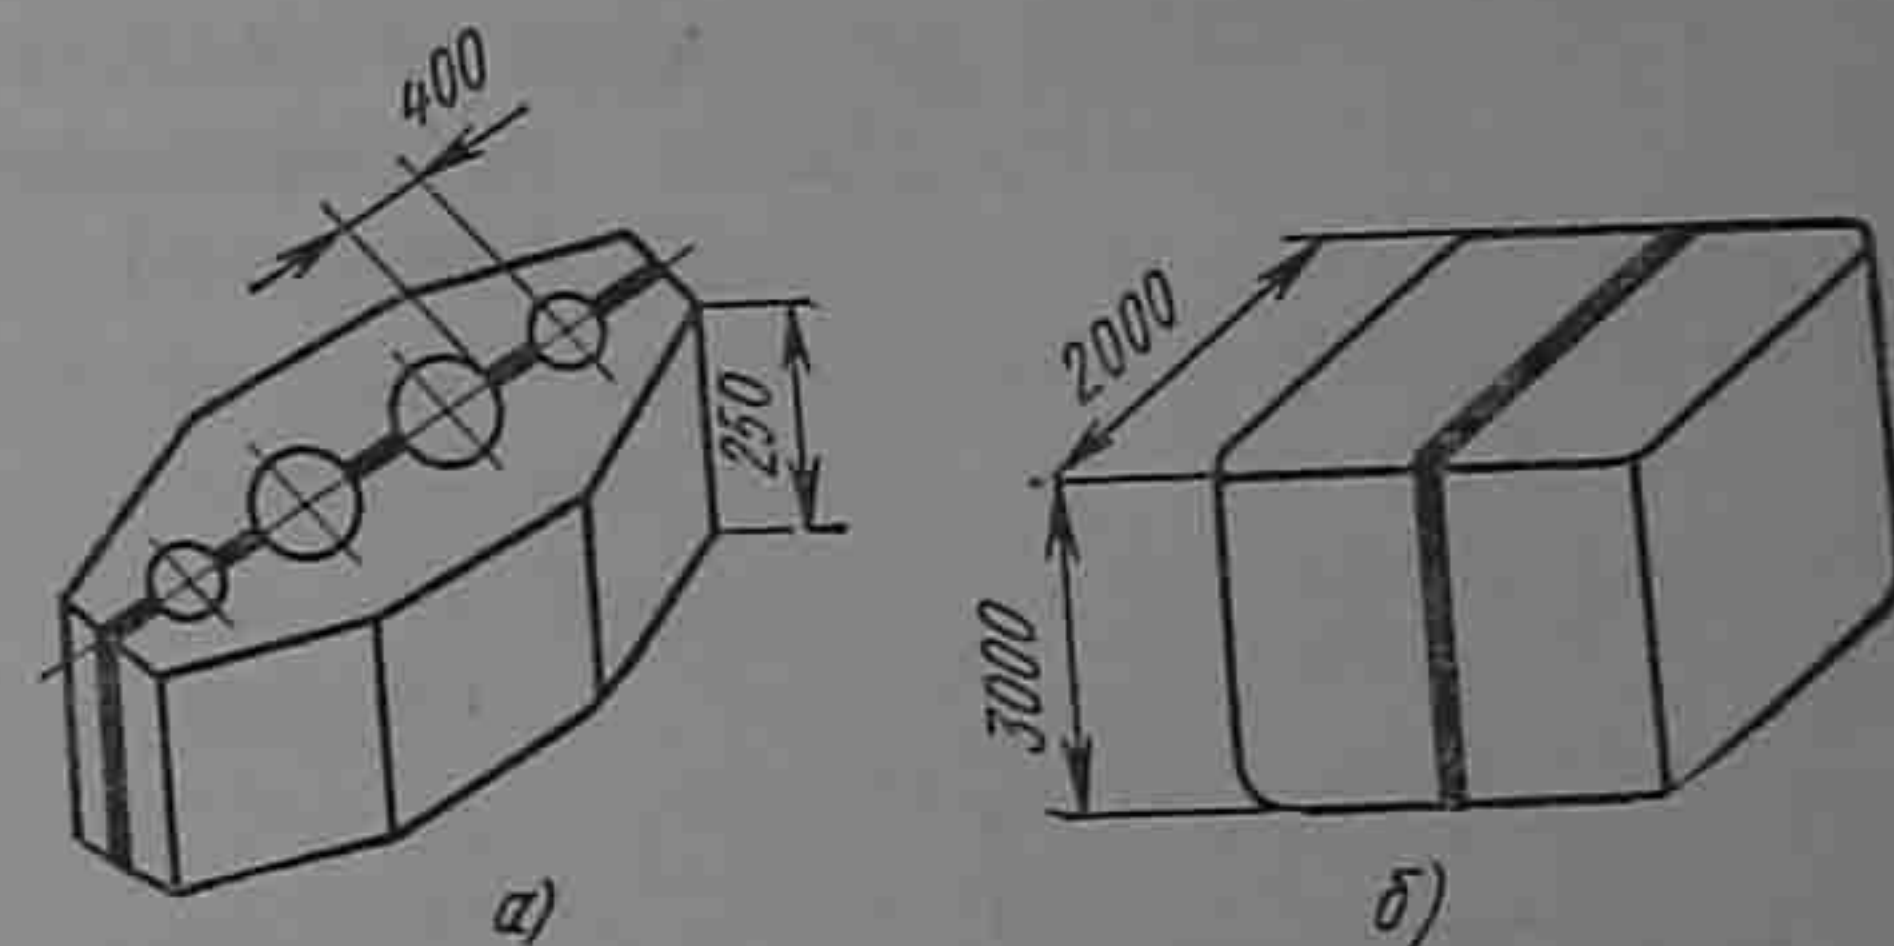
Примеры применения электрошлаковой сварки:
